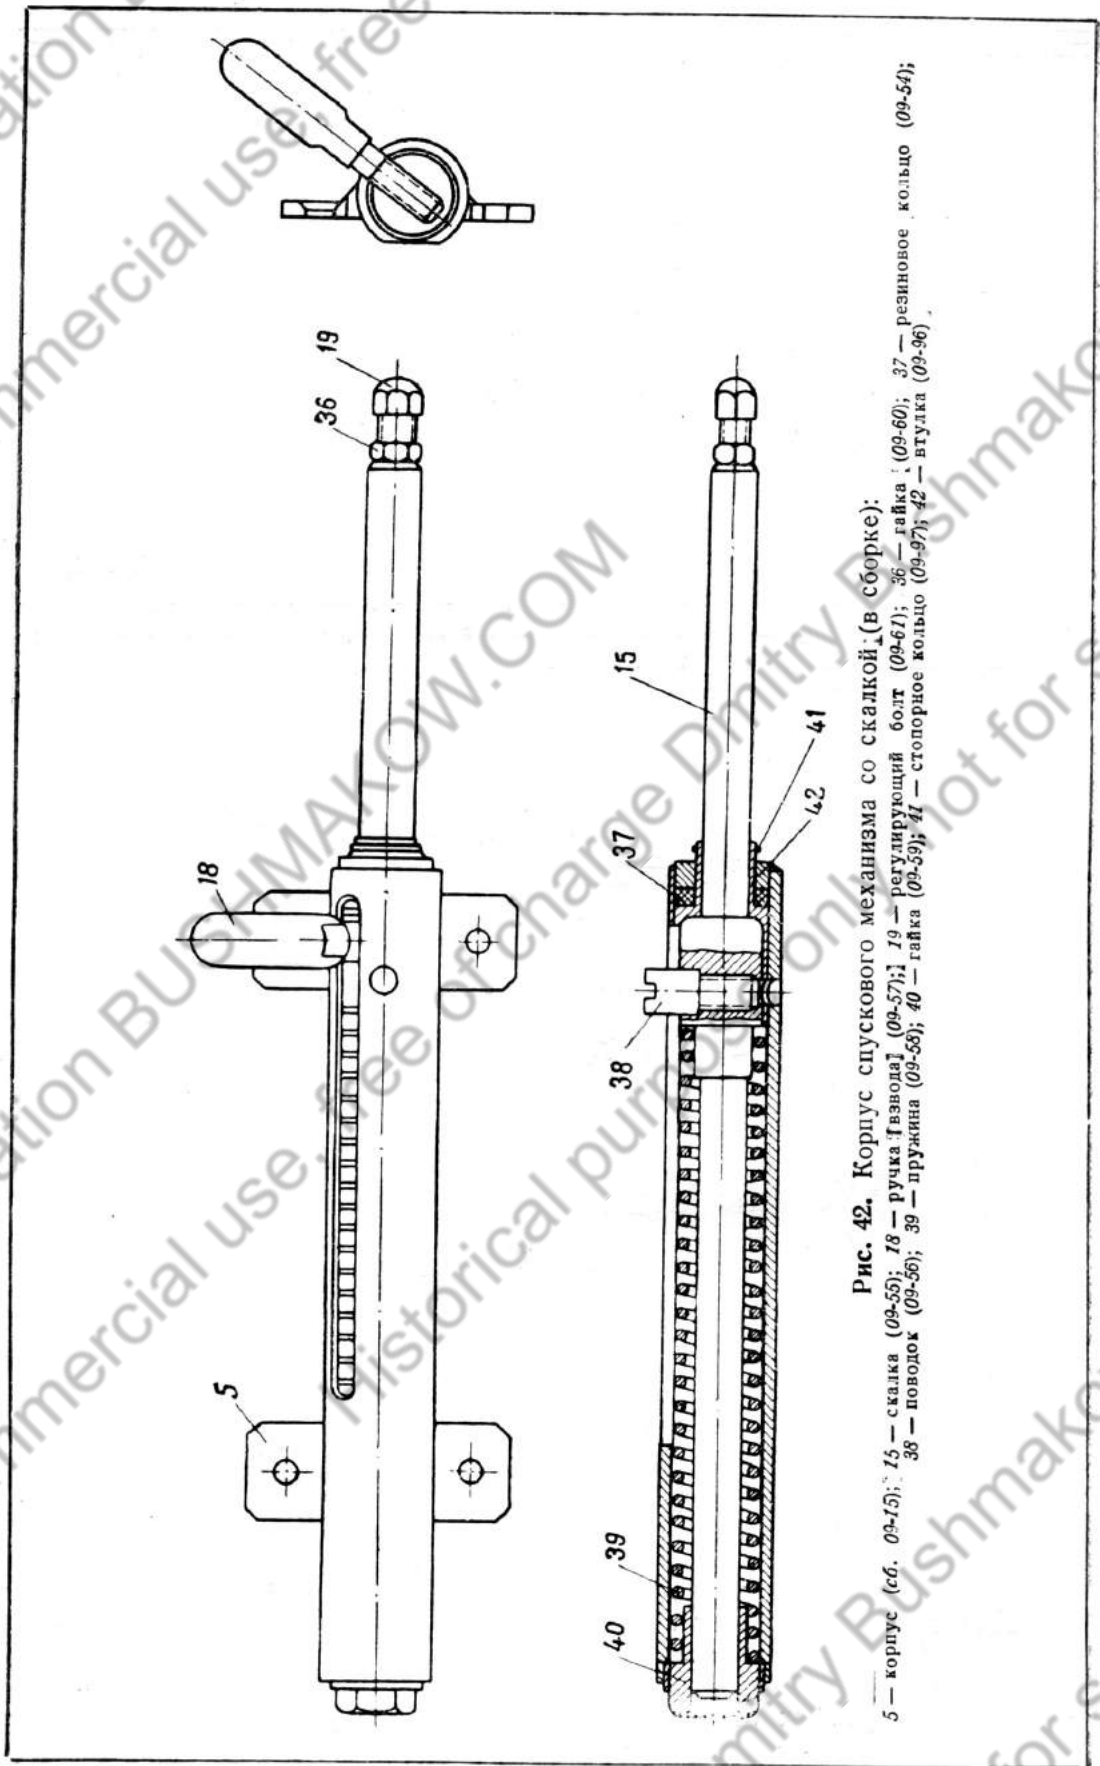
Корпус спускового механизма со скалкой (в сборке):
